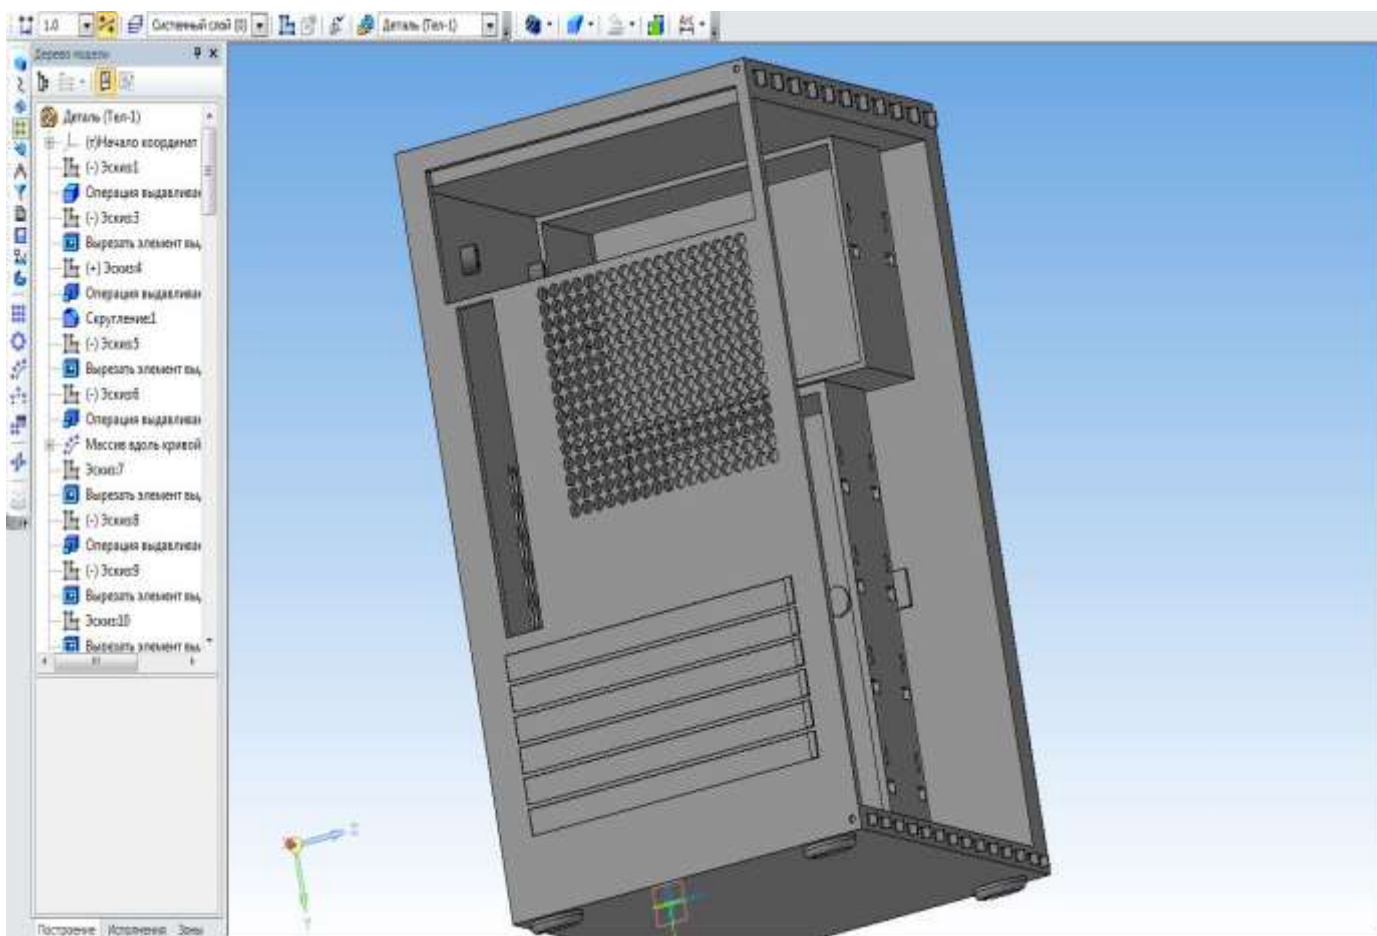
«3D сборка системного блока ПК», 3D сборка – системный блок
